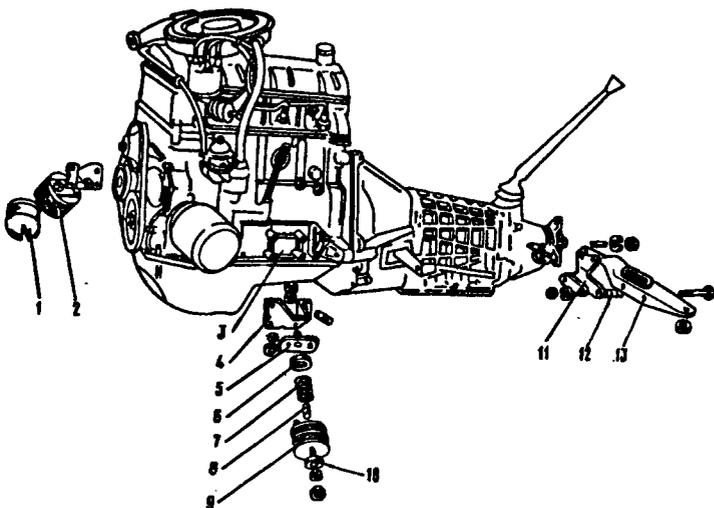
Подвеска двигателя: 1 - кожух опоры; 2 - опора передней подвески двигателя; 3 - фланец блока цилиндров; 4 - кронштейн; 5 - промежуточная пластина; 6 - изолирующее пластмассовое кольцо; 7 - пружина опоры; 8 - буфер; 9 - подушка опоры; 10 - шайба; 11 - опора задней подвески двигателя; 12 - дистанционная втулка; 13 - поперечина задней подвески двигателя
